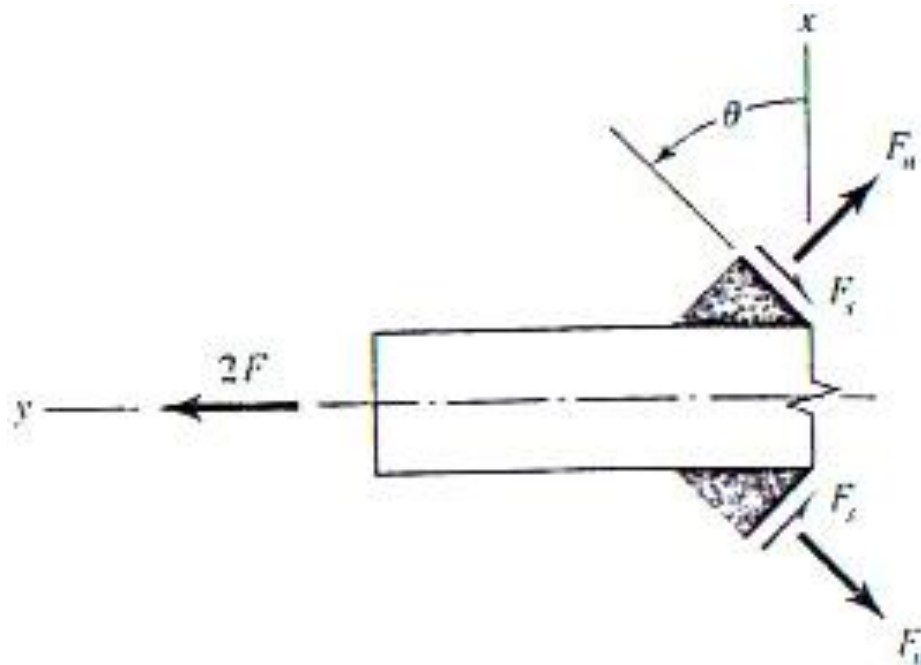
DIAGRAMA DE CUERPO LIBRE DEL CORDON DE LA SOLDADURA DE FILETE (Ref. 7)
